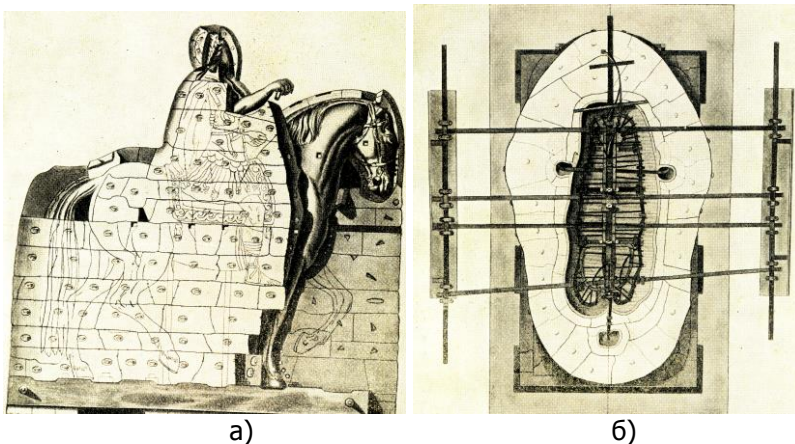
Вертикальный разрез кусковой формы (а) и горизонтальный разрез гипсовой формы с металлическим каркасом для крепления стержня (б)
